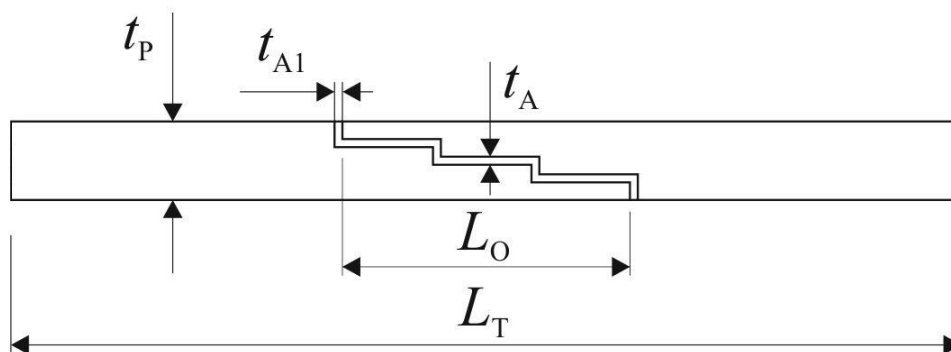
Geometria e respetivos parâmetros dimensionais da junta em degrau.
